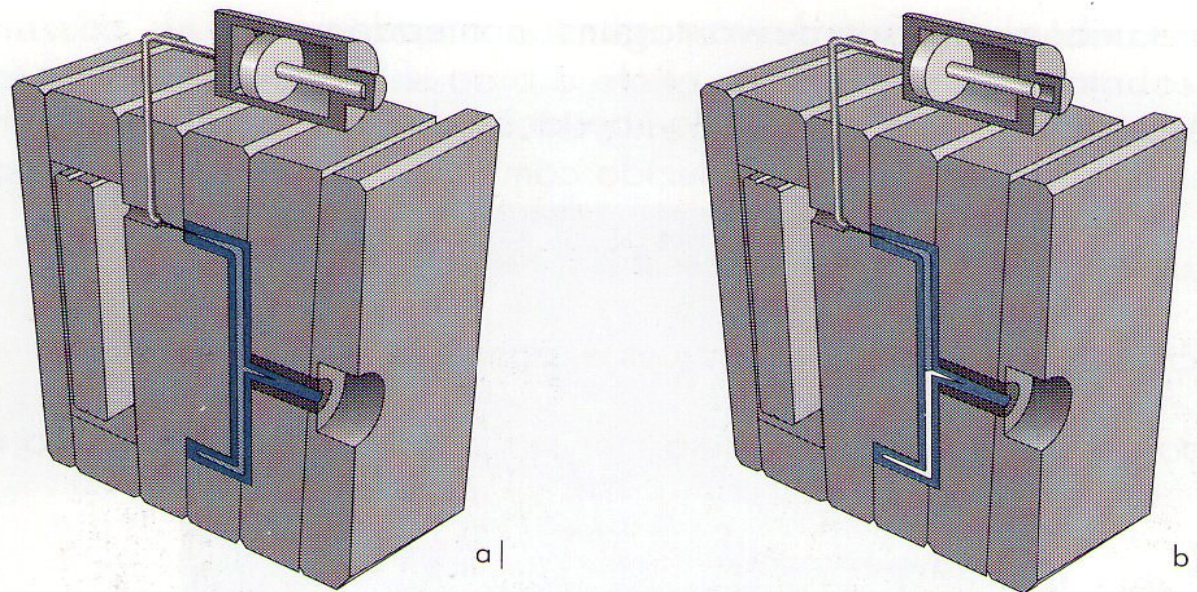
Moldação com gás a partir de agulha no molde
